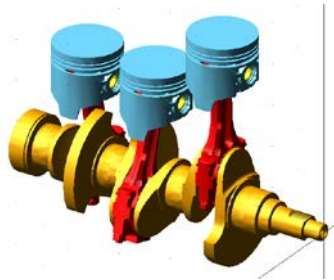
Modelo en ADAMS/View de un motor de combustión interna alternativo de 3 cilindros en línea
